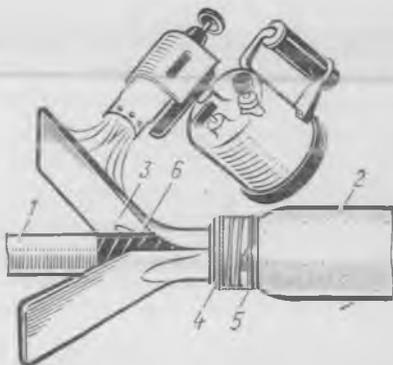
Сварка поливинилхлоридной оболочки медными вкладышами:
